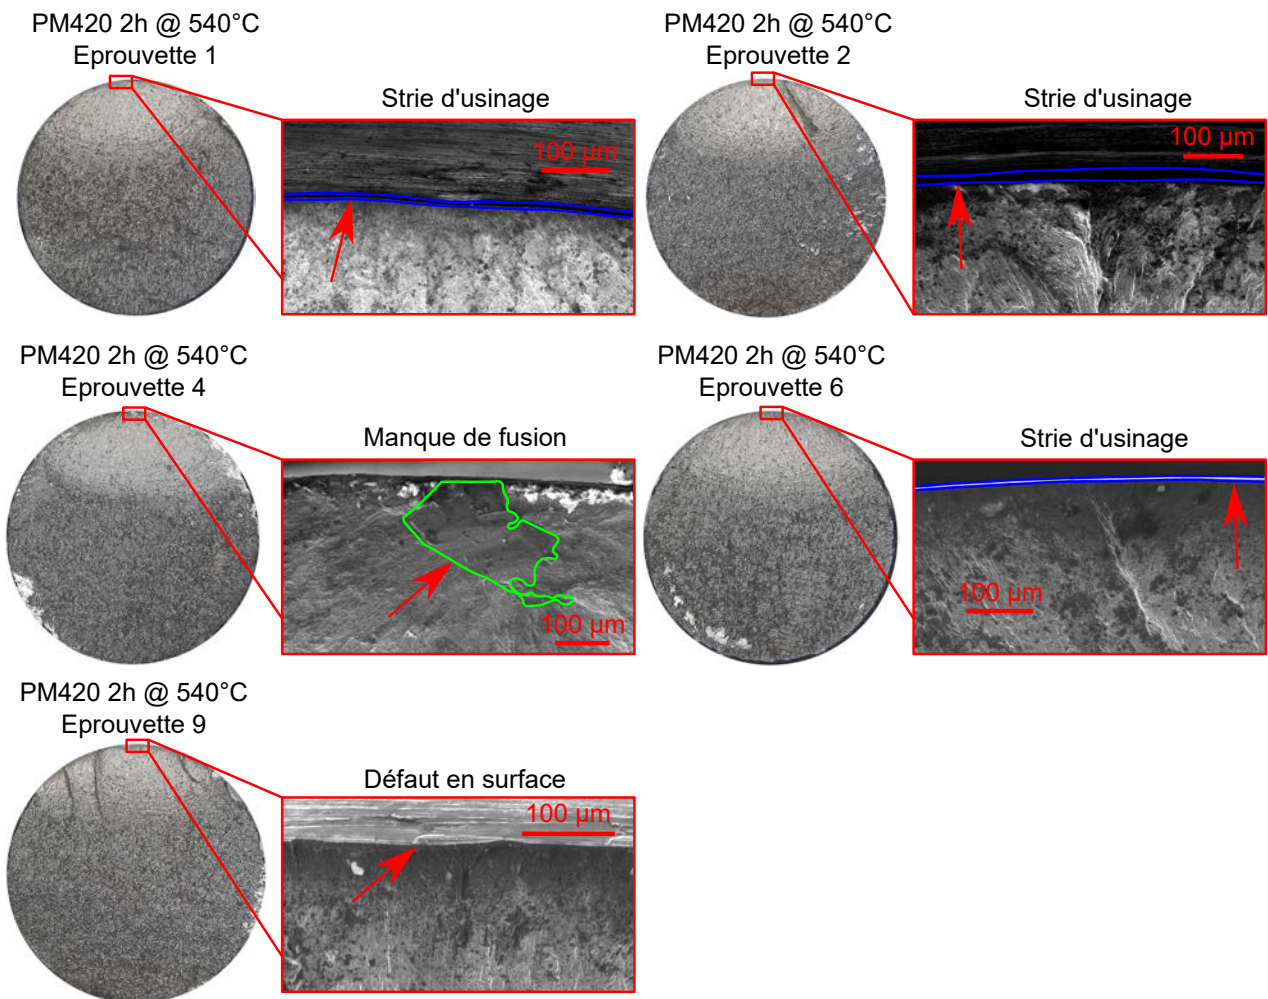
Faciès de rupture et défauts critiques observés sur les éprouvettes de PM420 usinées, toilées et revenues à 540°C pendant 2h
